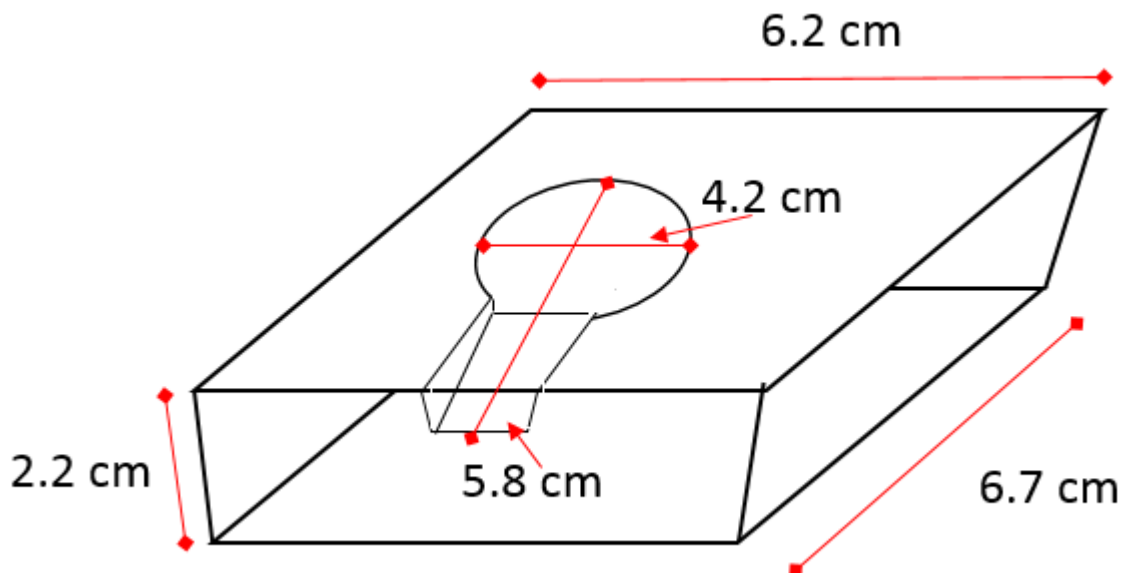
Diseño del molde de cobre para obtención de probeta.
